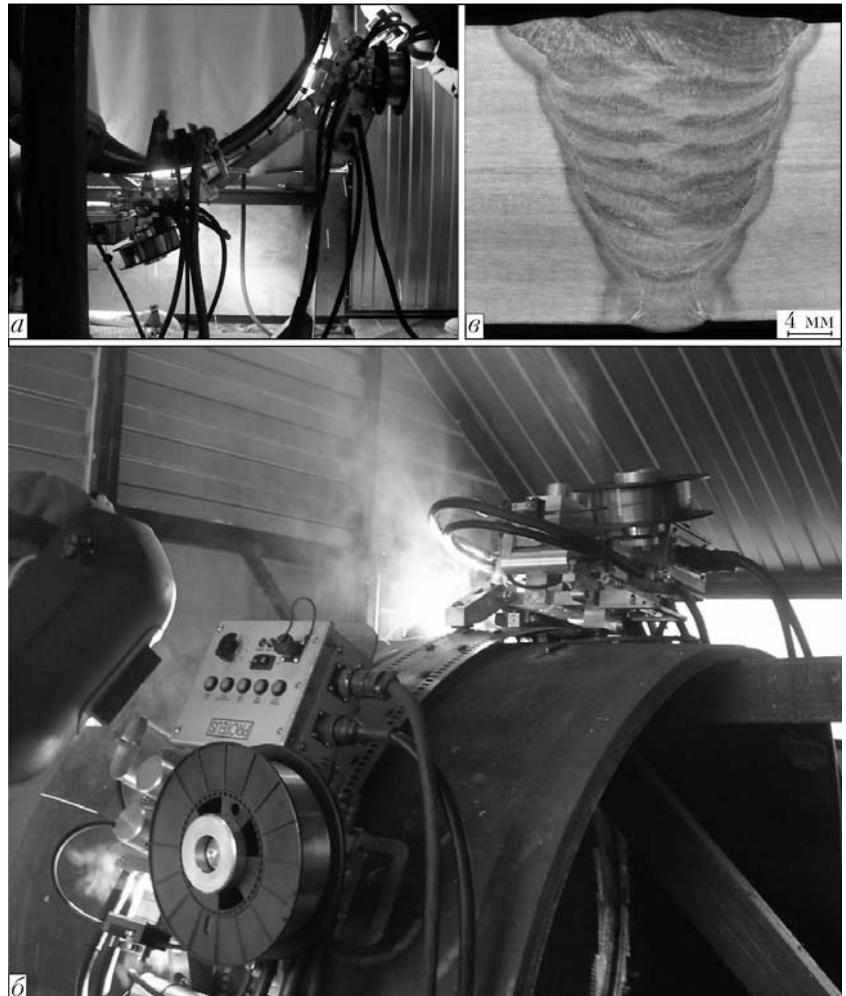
Начало (а) и конец (б) процесса автоматической сварки неповоротного стыка трубопроводов на комплексе «ПРОТЕУС» и шлиф сварного соединения трубопровода из стали K65 толщиной 27,7 мм (в)
